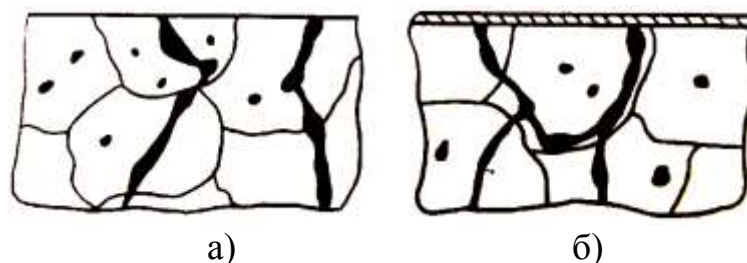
Схема запрессовки сквозных дефектов в отливке: *а* – литейной или снятой коркой; *б* – после абразивоструйной обработки
